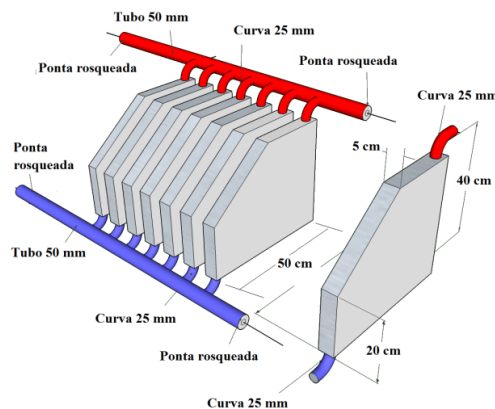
Conjunto de placas paralelas de parede dupla, para aquecimento do fluido quente.
